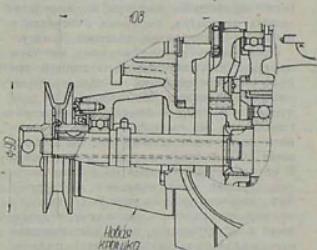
Насадка шкива привода воздуховодки на полусиний вал двигателя М-72.
